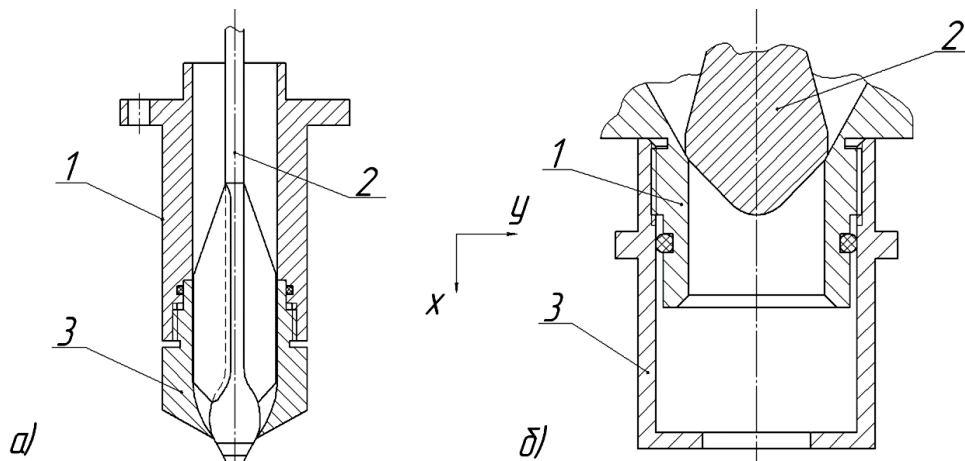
Конструкція робочого органу в вагових дозаторах: а) конічний; б) циліндричний: 1 – сідло; 2- клапан; 3 – корпус
